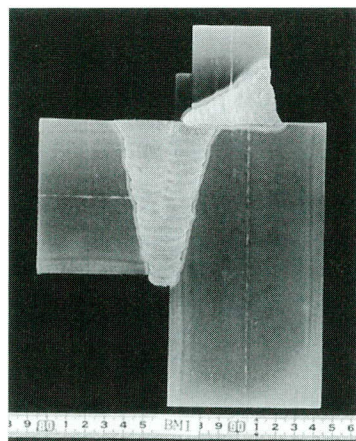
角溶接と梁溶接重複部マクロ試験
